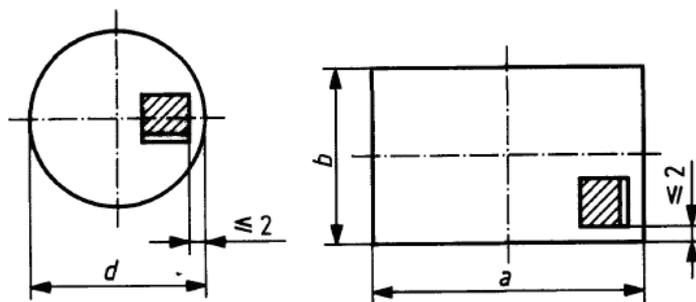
Расположение мест вырезки образцов для испытаний на ударный изгиб для круглого и квадратного сечений согласно Eurocode 10025–1
